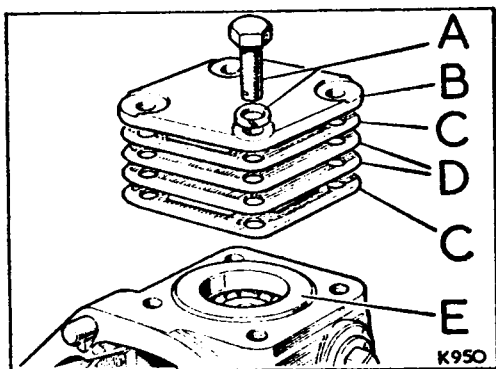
Tapa inferior de la caja de engranajes.
